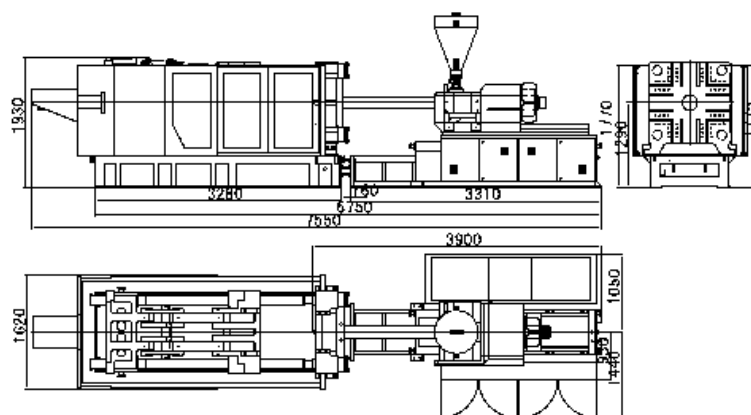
Desenho da máquina de injeção (Adaptado de [38])
